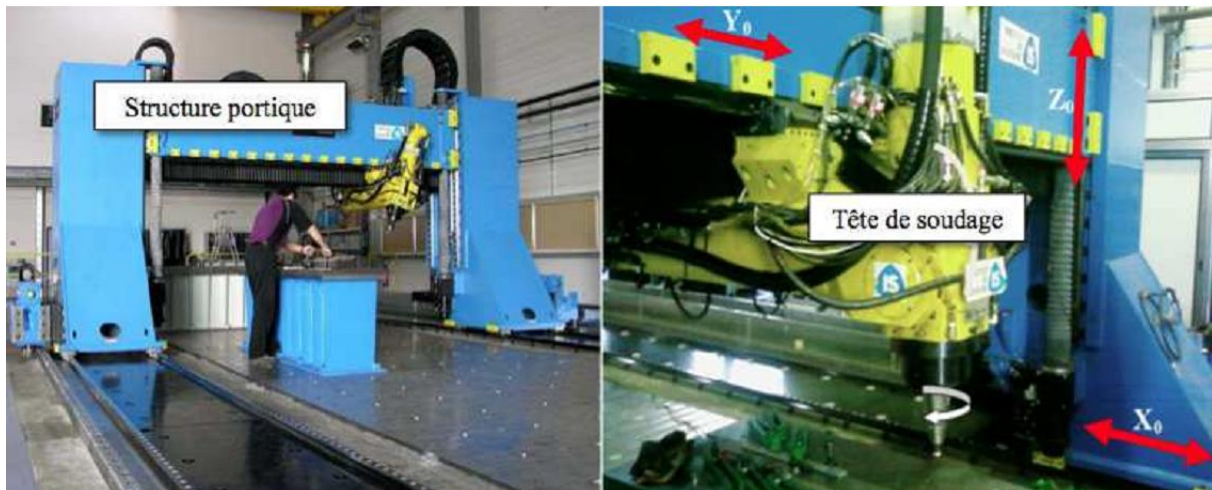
Une Machine FSW (MTS) de l'institut de soudure [Nejah .06].
